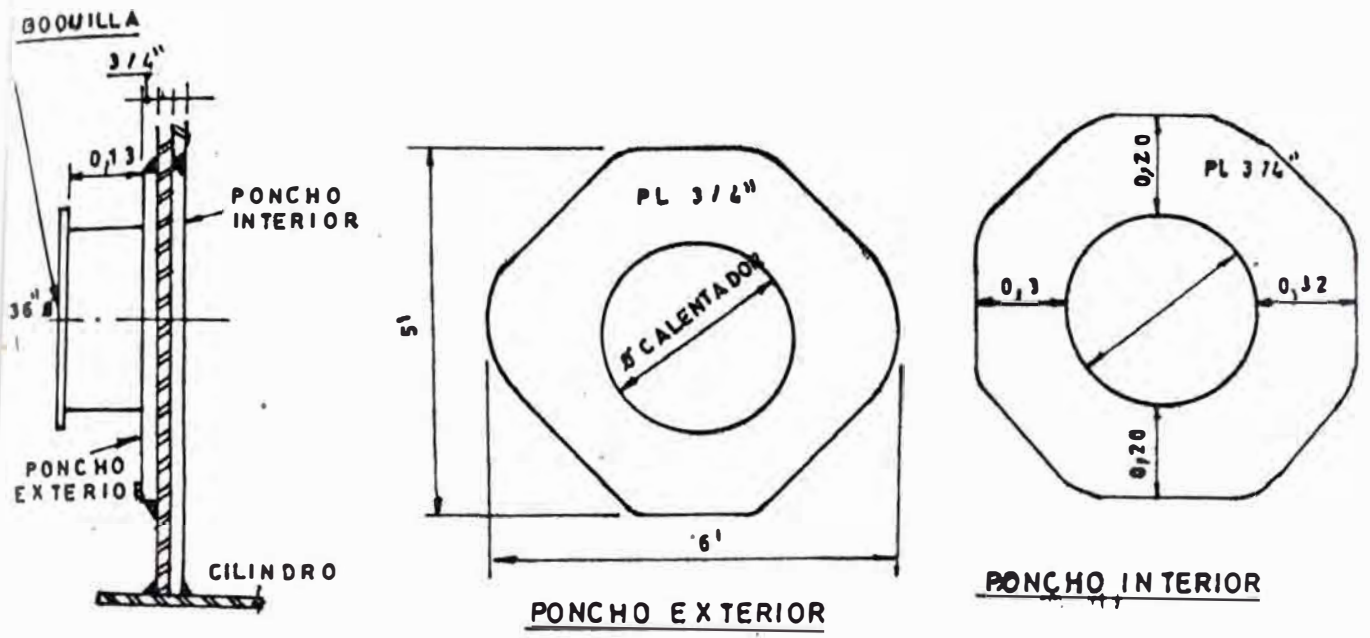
PLANCHAS DE REFUERZO A BOQUILLAS DEL CALENTADOR TK 258
